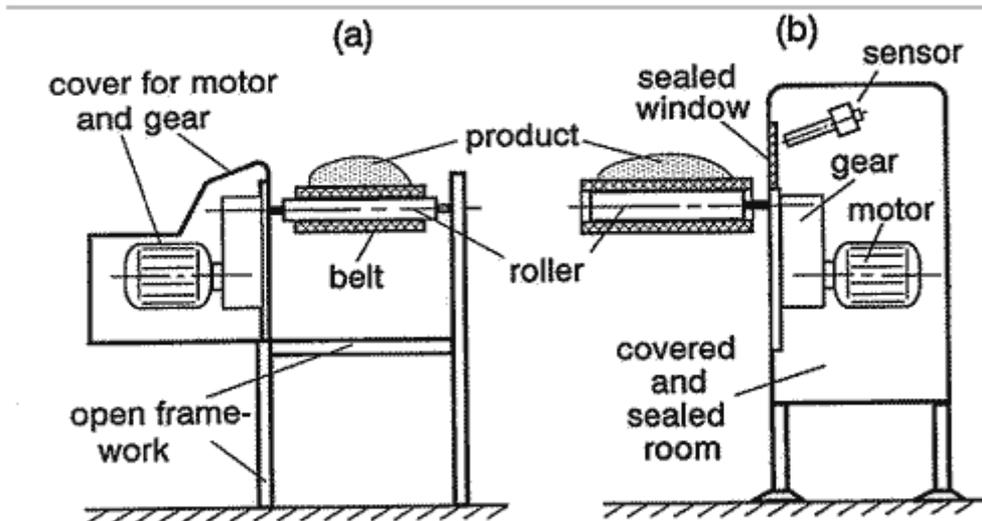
Защитные кожухи для приводов. (а), Для предохранения продукта от загрязнения приводом и двигателем, их следует покрывать защитным кожухом, оставляя область опорной станины открытой для очистки; (б) герметичный кожух для двигателя, передаточных механизмов и опорной станины создает открытый доступ к ленте и роликам.
